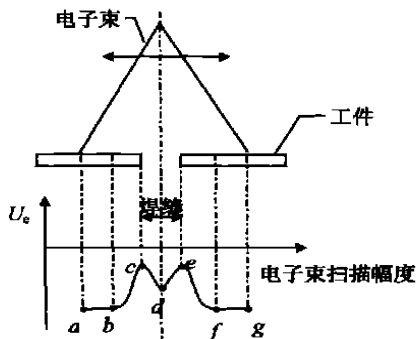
电子束扫描焊缝时产生的焊缝信号以及束斑在工件表面的对应位置
